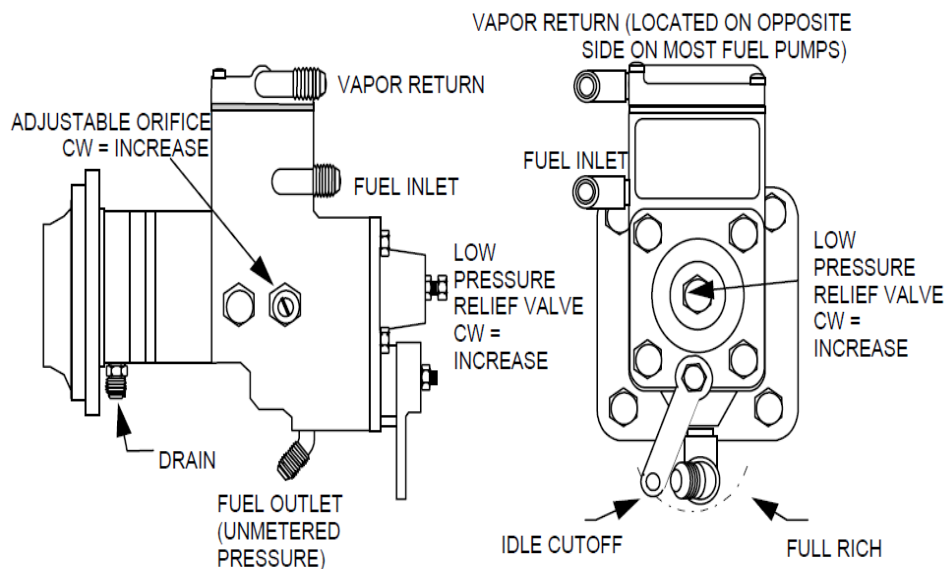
Bomba de combustible equipado con el control de mezcla
